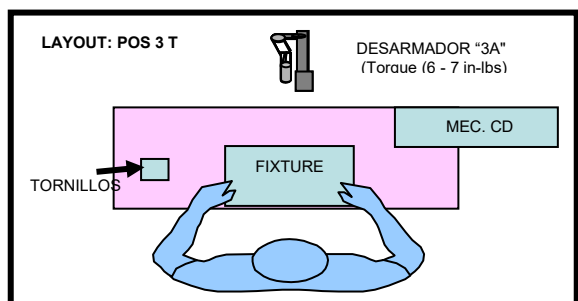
Presentación de partes de la línea final de T, posición 3
